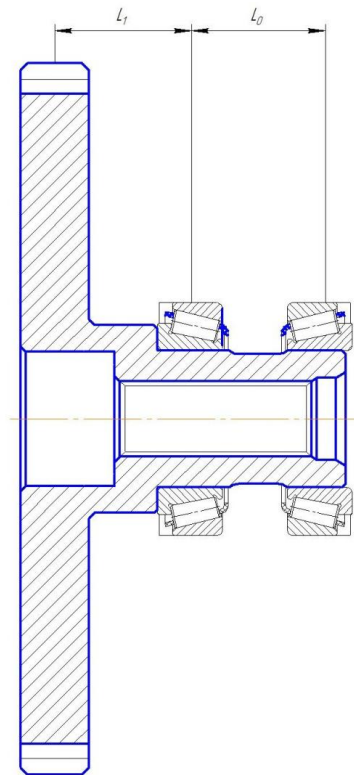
Компоновка ведущего вала заднего колесного редуктора
